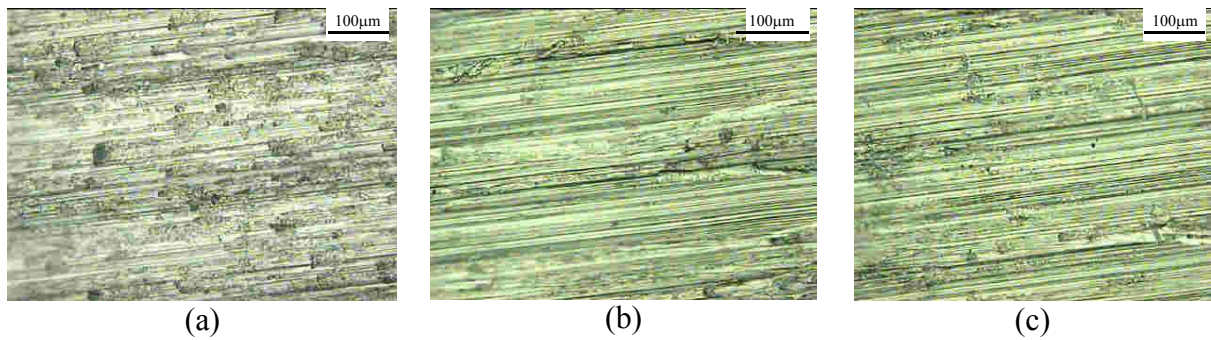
Superfícies usinadas com profundidade de corte de 0,6 mm dos aços (a) 303, (b) 304 e (c) 310. Microscopia óptica.
